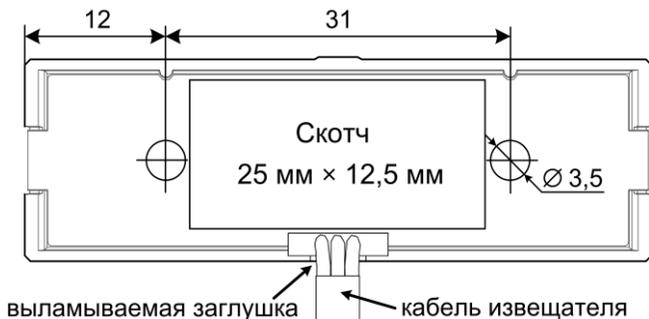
Основание ПОЛЮС-GL mini. Место наклеивания скотча. Присоединительные размеры и расположение отверстий для монтажа
